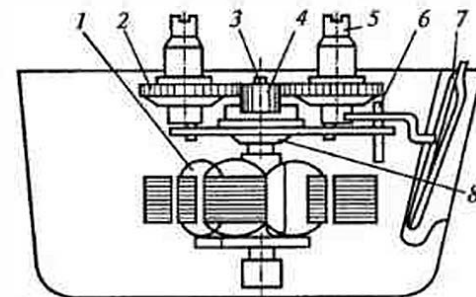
Конструкция узла привода зубчатых колес бритвы «Харьков-15М»
